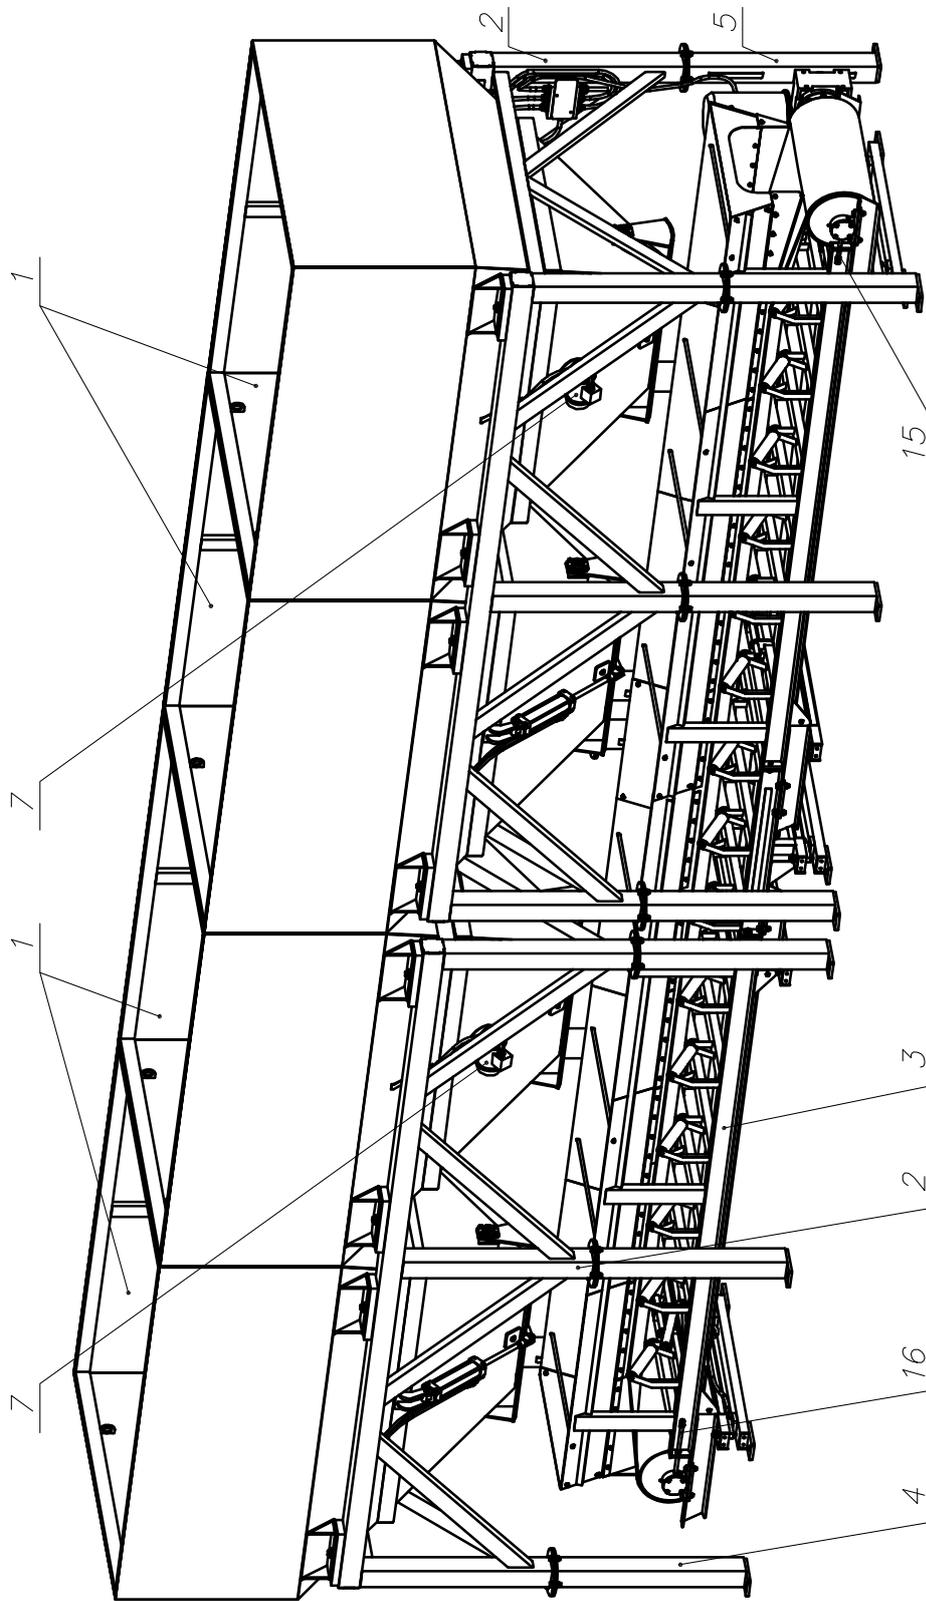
Общий вид дозатора ДЗ-28 вид спереди.
